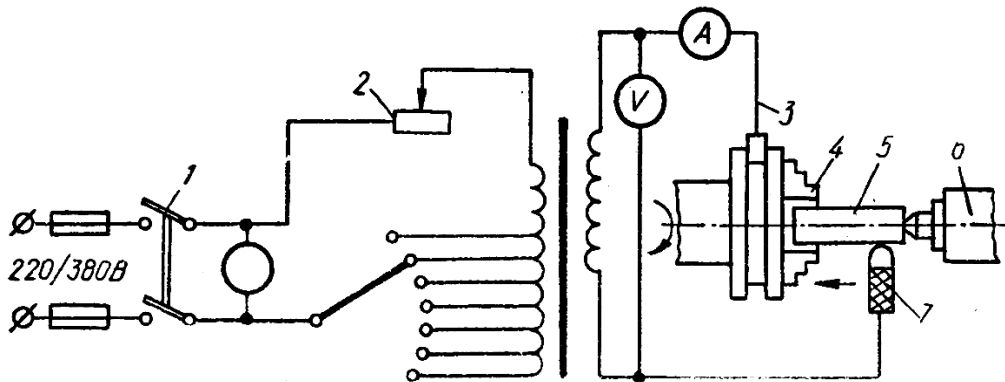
Принципова схема установки для електромеханічної обробки: 1 – рубильник; 2 – реостат; 3 – провід вторинної обмотки; 4 – патрон верстата; 5 – деталь; 6 – задня бабка верстата; 7 – інструмент для обробки.
